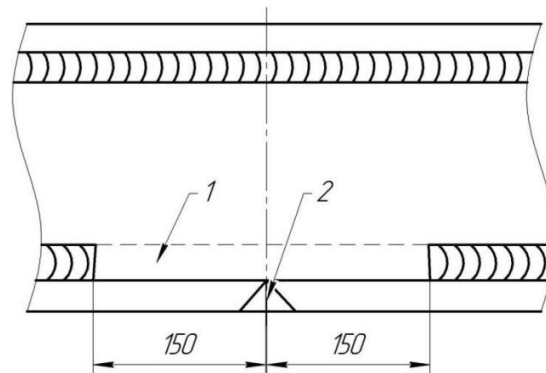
Схема підготовки до заварювання тріщини в полці балки коробчастого перерізу
